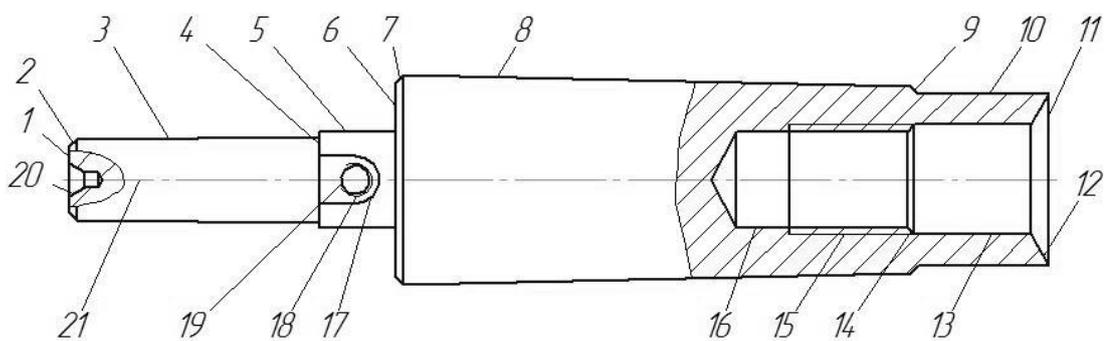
Эскиз корпуса насадного режущего инструмента
